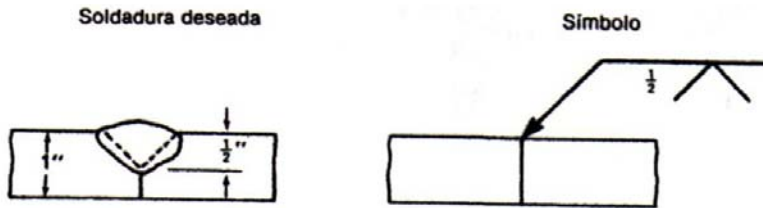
Símbolo de soldadura en el que no se especifica la penetración.
